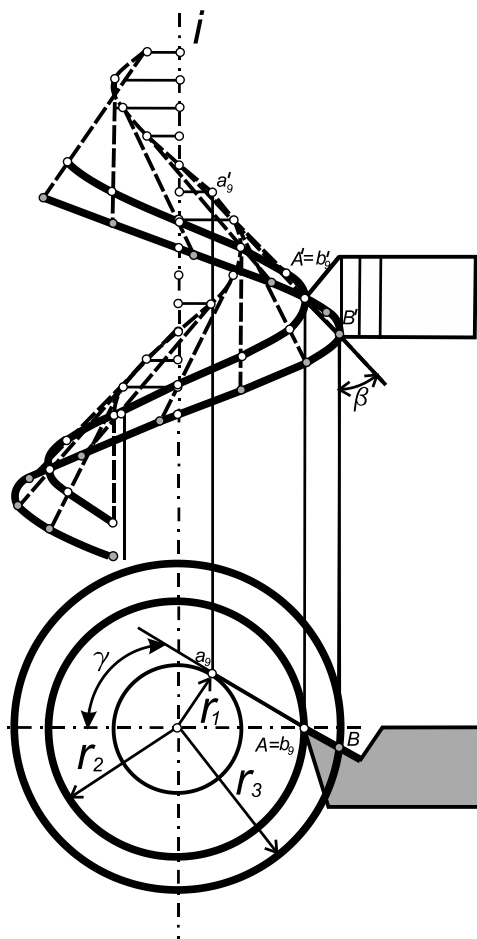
Схема формування конволютної різьбової поверхні різцем з прямолінійною різальною кромкою, що не лежить у осевій площині заготовки
